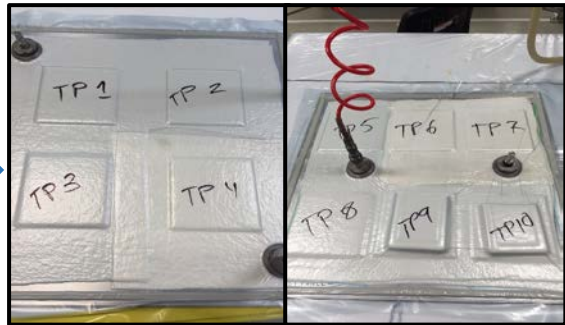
Izquierda. Proceso sin utilizar caul plates. Derecha. Plenum utilizando caul plates.
